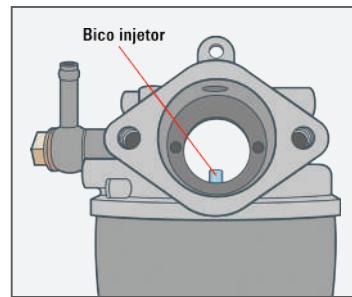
Ilustração de um bico injetor de combustível do carburador
